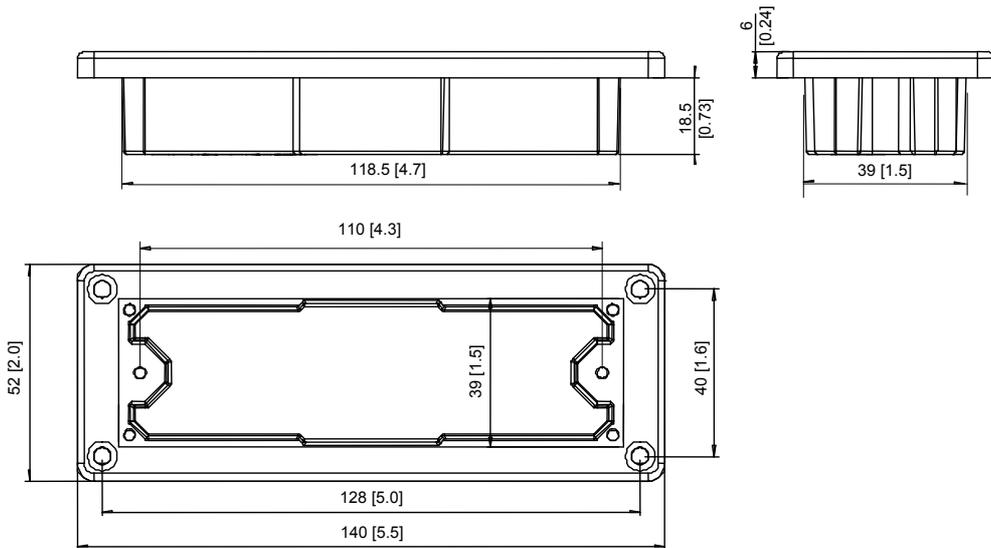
Dimensiones en mm [inch] de la caja de montaje del panel de control remoto ICC y el panel de control remoto APC
